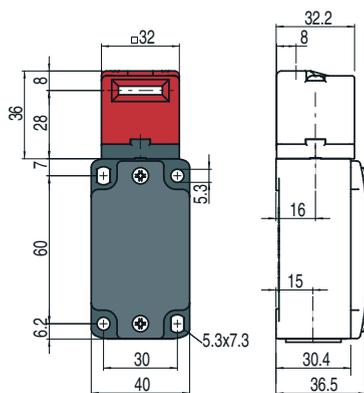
Dimensiones del S200-Mxxx-M20
